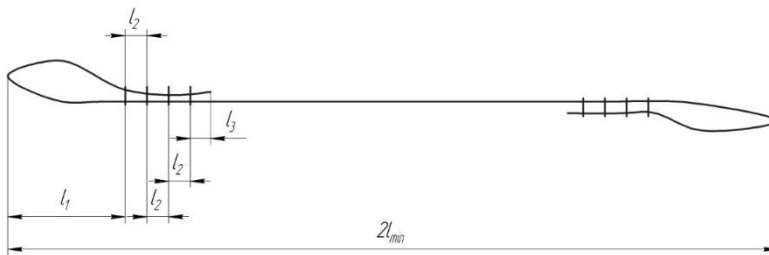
Розрахункова схема для визначення довжини заготовки
